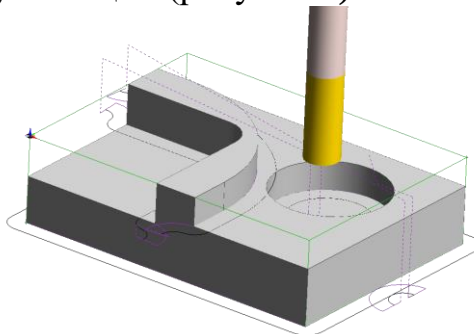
Визуализация процесса фрезерования корпуса.
